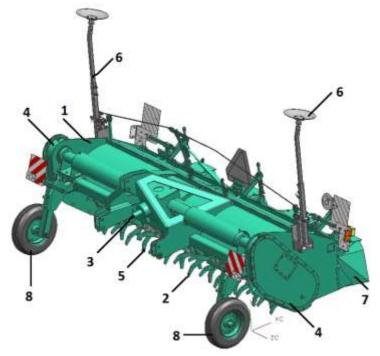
Общий вид агрегатов АПК 1 — рама; 2 — ротор; 3 — редуктор конический; 4 — бортовая передача; 5 — зубья; 6 — маркер; 7 — гребнеобразователь; 8 — колеса.
